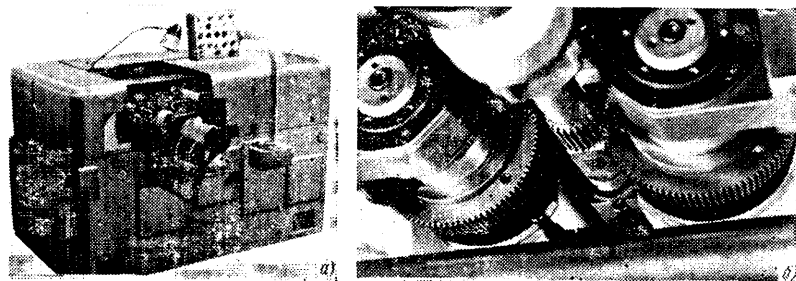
Полуавтомат мод. 5А965 для обкатывания зубчатых профилей: а — общий вид станка; б — зона обработки
